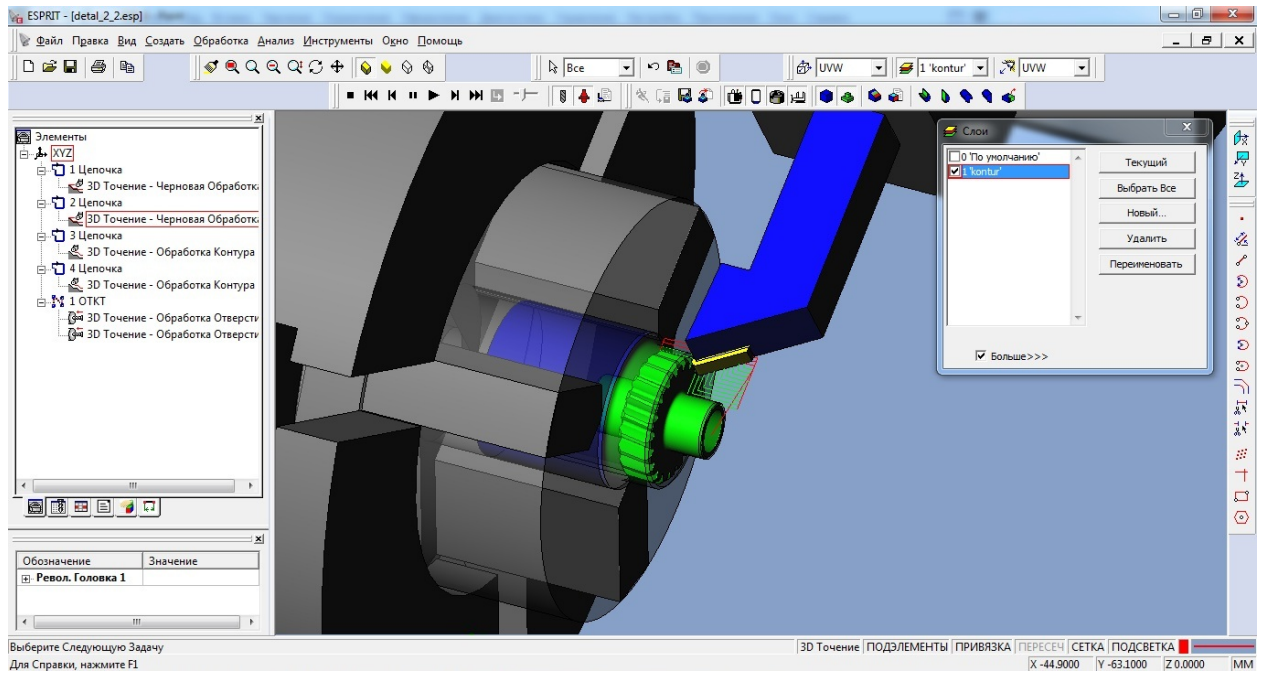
Траектория ruchu металорізального інструменту при обробленні контуру вала-шестерні
